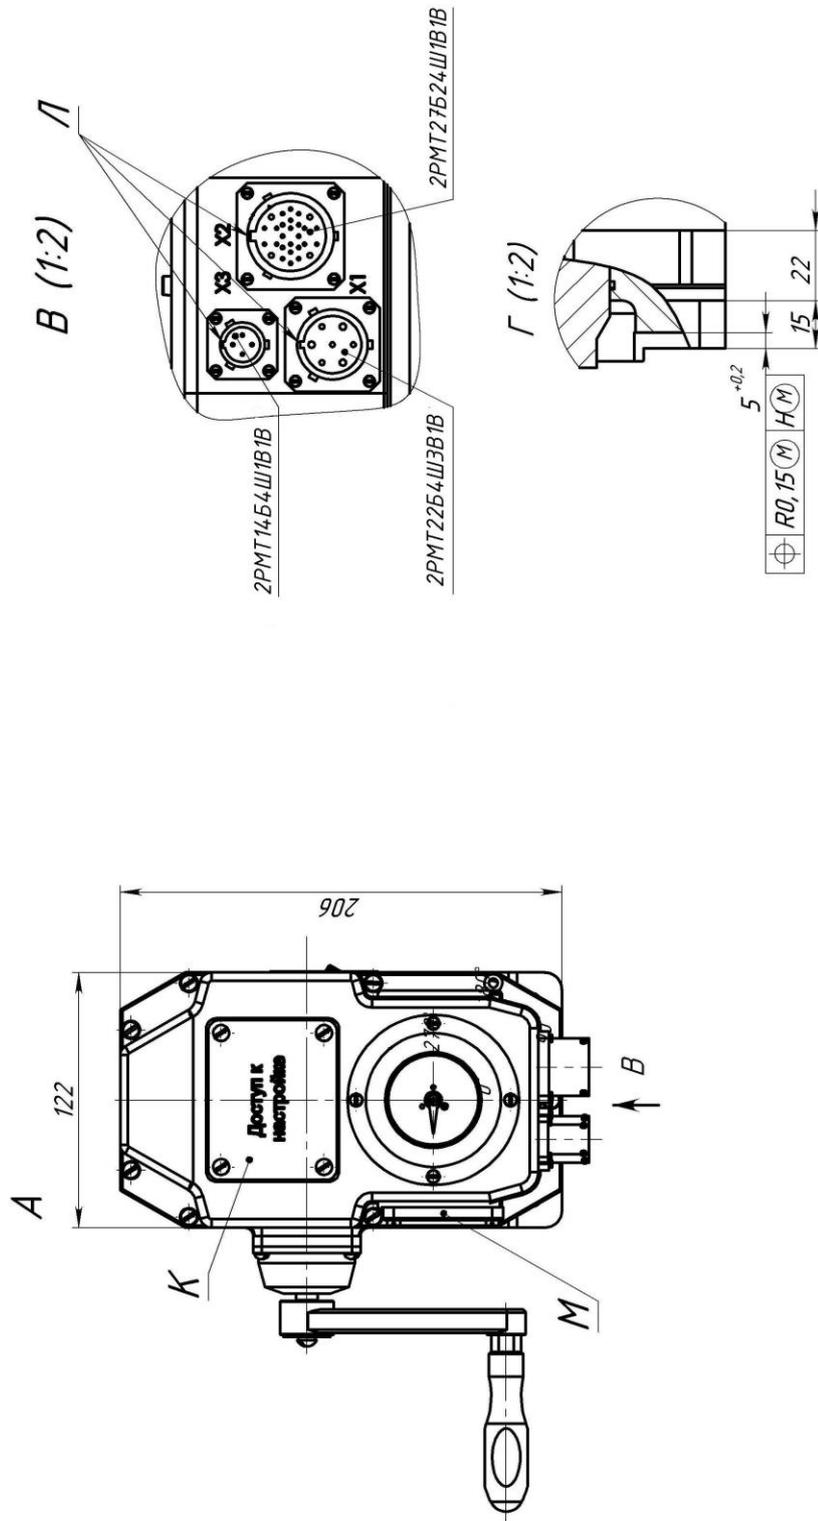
Габаритный чертеж привода М30У-500/5-0,25ТМ
